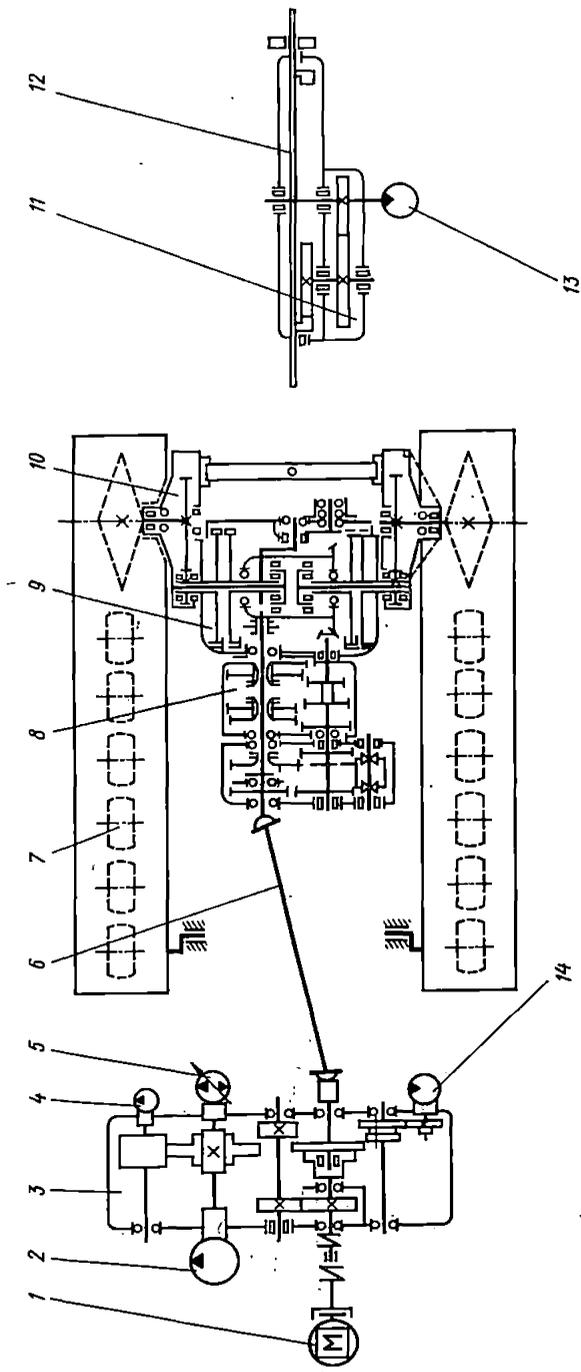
Кинематическая схема экскаватора ЭТР-134:
